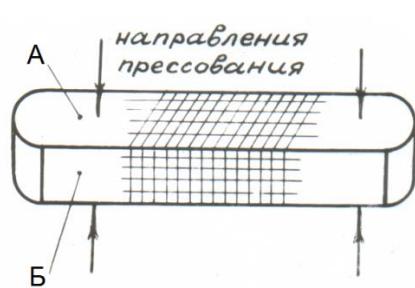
Схема расположения координатной сетки на образце для изгиба
